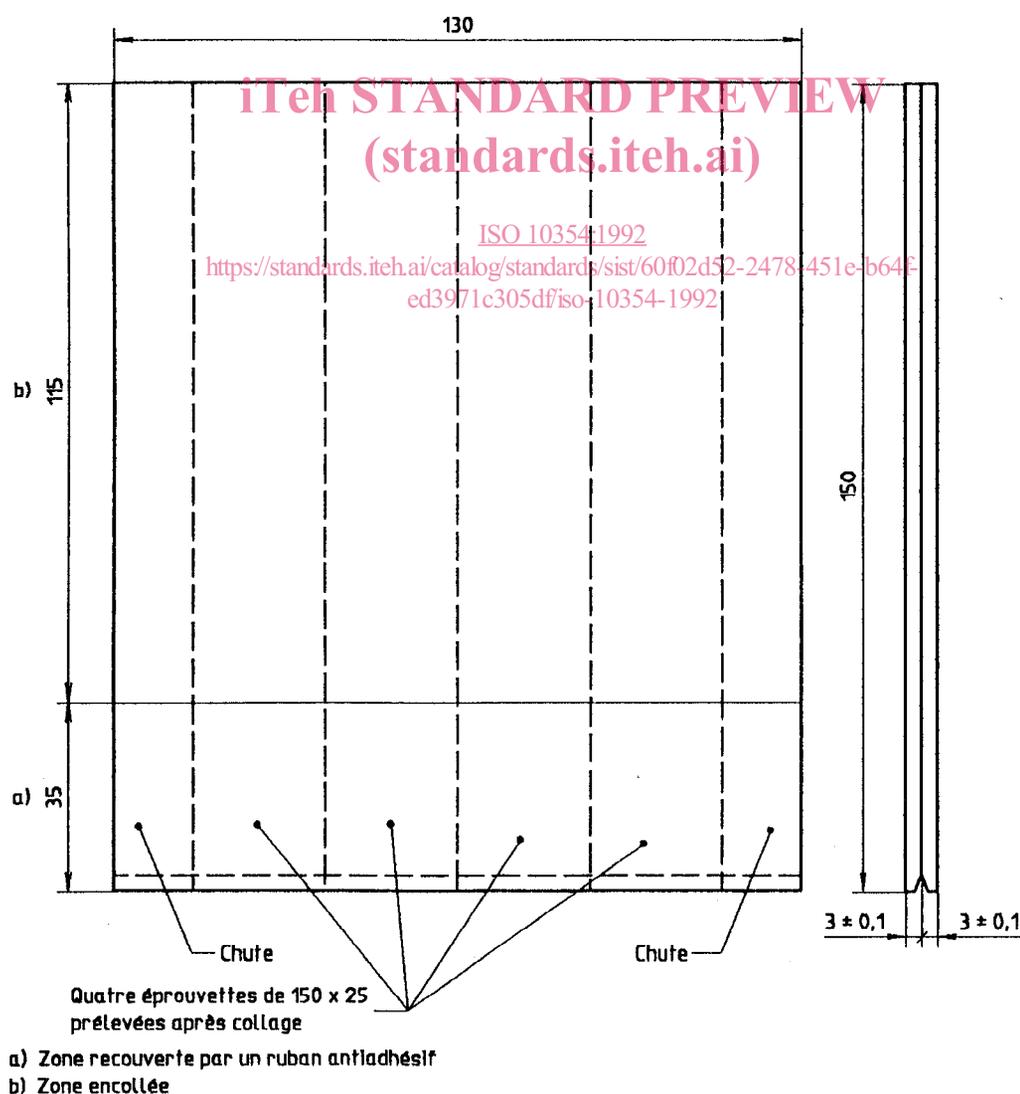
Dimensions d'une plaque collée à partir de laquelle sont découpées les éprouvettes
